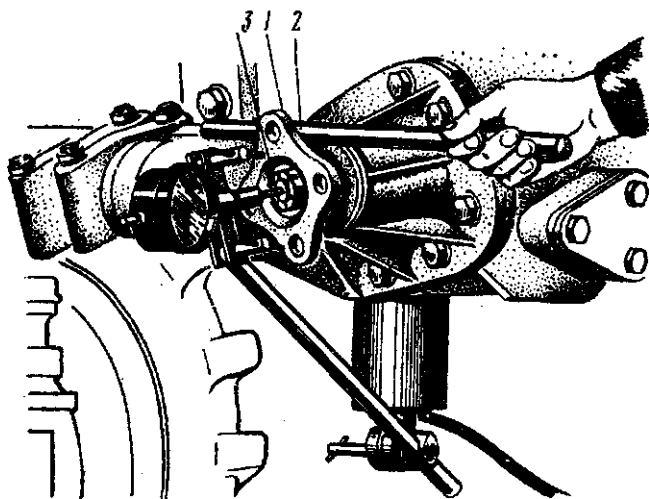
Вимірювання осьового зазору в підшипниках шестерні головної передачі переднього моста трактора МТЗ-82 за допомогою пристрою КИ-4850: 1 - фланець стакана; 2 - ломик; 3 - шток пристрою.
